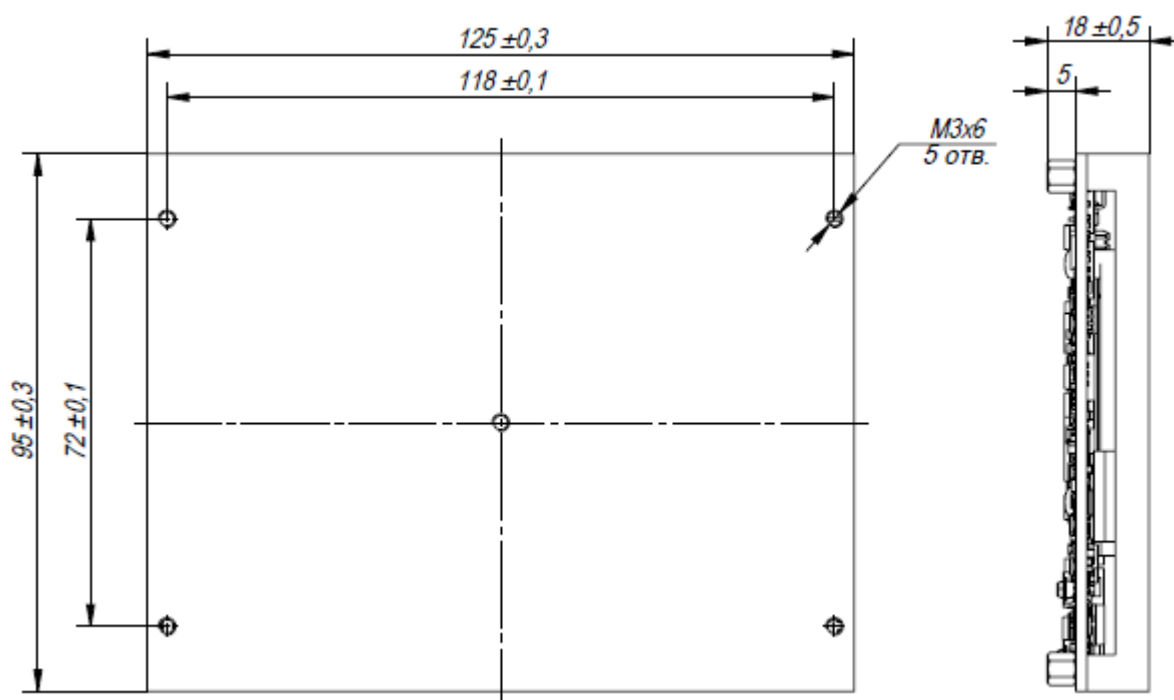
1 - Габаритные и присоединительные размеры изделия
